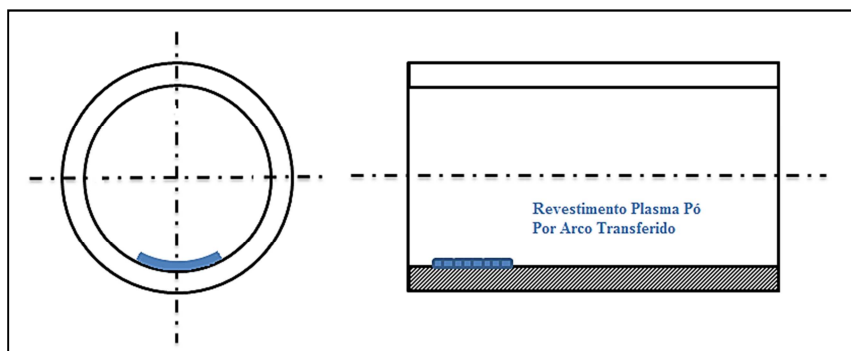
Segmento de material depositado (Inconel 625) sobre diâmetro interno de tubo de aço carbono pelo processo de soldagem de revestimento plasma pó.
